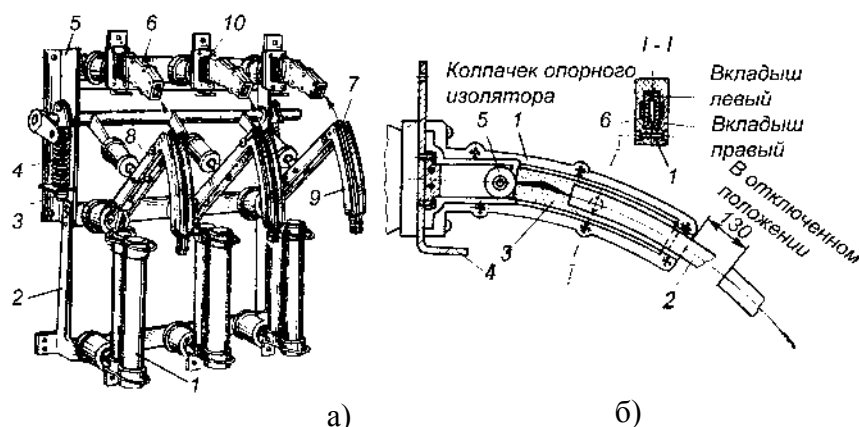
Выключатель нагрузки ВНП-16 на 10 кВ: а) – общий вид: 1 – предохранители ПК; 2 – полурама; 3 – резиновые шайбы; 4 – отключающие пружины; 5 – рама; 6 – дугогасительная камера; 7 – подвижный дугогасительный контакт; 8 – подвижный рабочий контакт; 9 – скоба; 10 – неподвижные контакты; б) – разрез гасительной камеры: 1 – щеки гасительной камеры; 2 – контактный нож; 3 – вкладыш из органического стекла; 4 – неподвижный рабочий контакт; 5 – неподвижный дугогасительный контакт; 6 – дуговой паз
